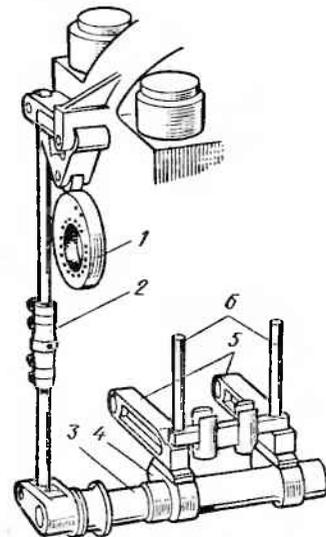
Двухпозиционный привод нижнего выталкивателя (обозначения см. рис. 64)
